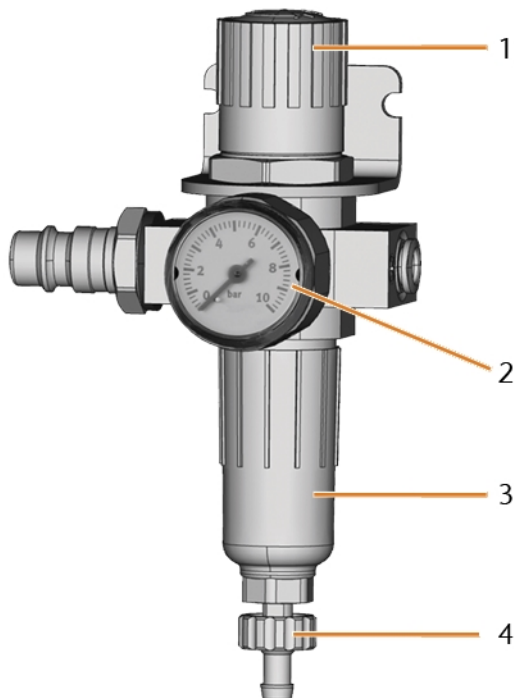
DRUCKMINDERER: DRUCKLUFT EINSTELLEN UND KONTROLLIEREN
